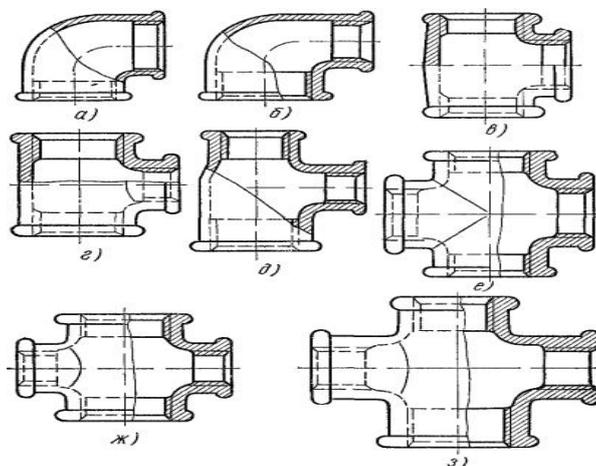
Соединительные части из ковкого чугуна для сборки труб под углом и устройства ответвлений:
